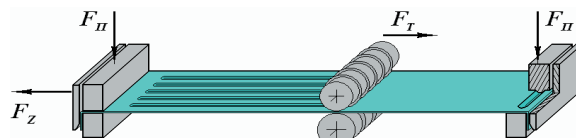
Способ изготовления профилей с плоскими концевыми участками
